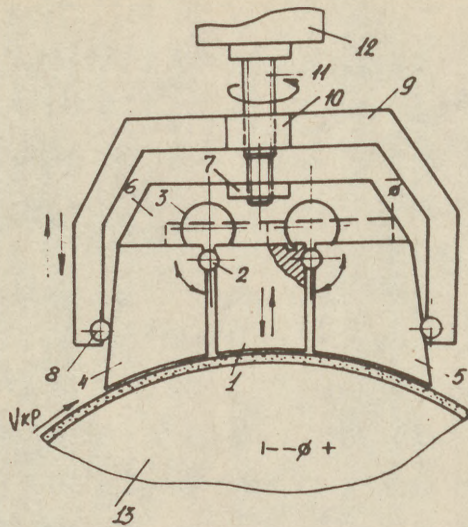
Схема устройства, реализующего способ управления режущей поверхностью алмазного круга с периферийным рабочим слоем
